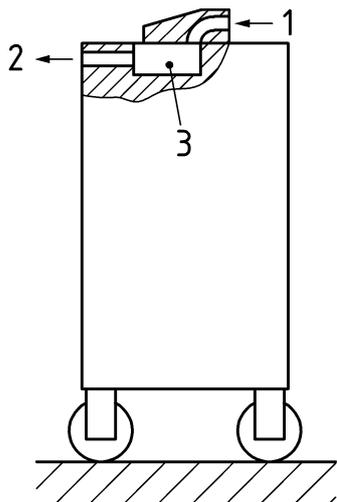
Füllmaschine mit Zylinder und KolbenBild 2 — Füllmaschine mit Einfülltrichter und Beschickungseinrichtung1.2.3 Vorsatzmaschinen für Füllmaschinen
